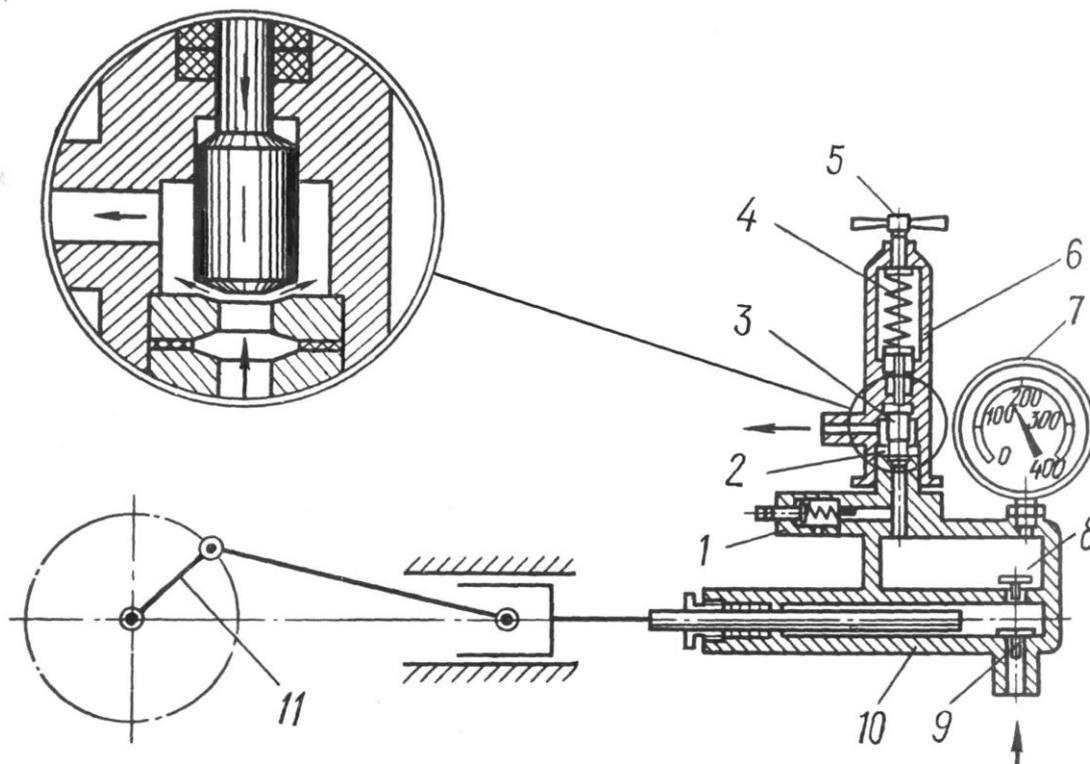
Гомогенизатор клапанного типа: 1 – предохранительный клапан; 2 – седло клапана; 3 – клапан; 4 – пружина; 5 – регулировочный винт; 6 – гомогенизирующий клапан; 7 – манометр; 8 – нагнетательный клапан; 9 – всасывающий клапан; 10 – насос; 11 – кривошипно-шатунный механизм
